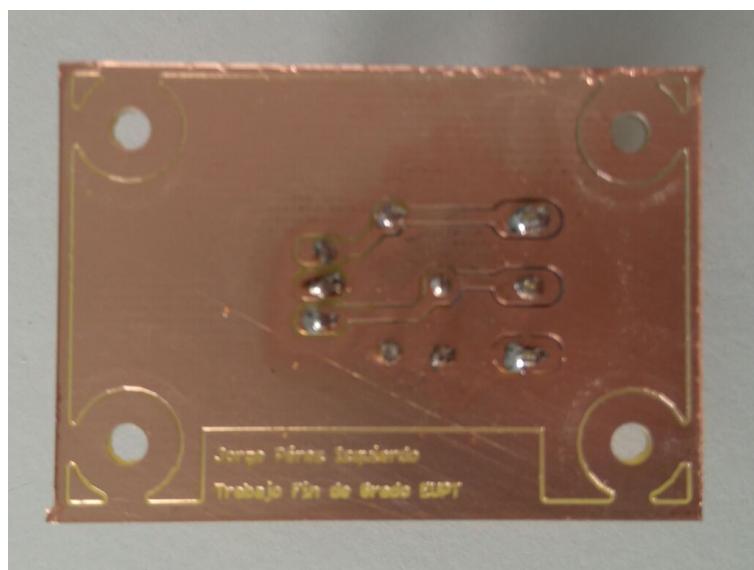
Placa de circuito impreso del regulador de tensión soldada.
